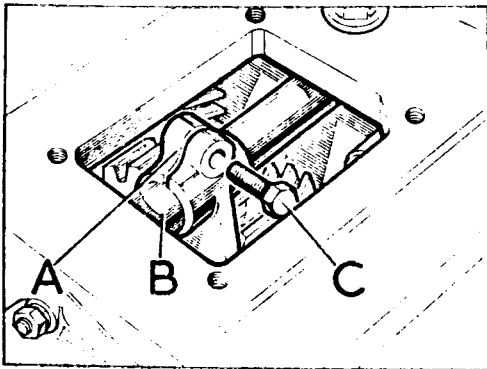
Conjunto de la horquilla selector de la caja reductora
